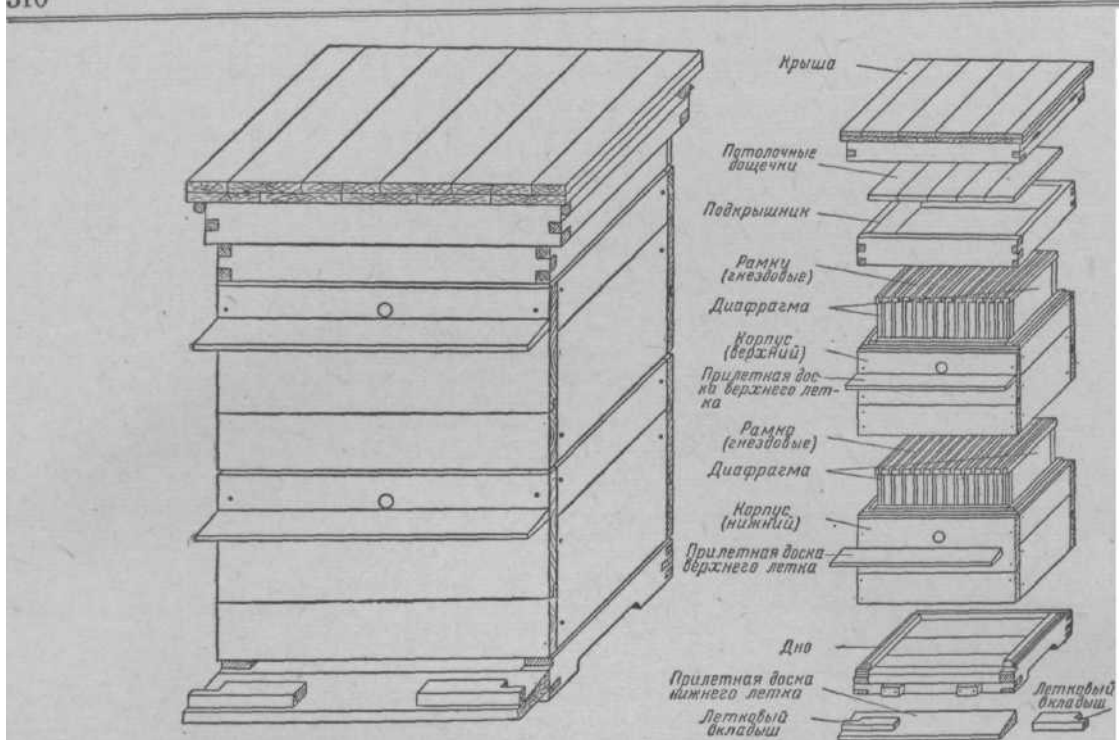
Одностенный двухкорпусный улей (общий вид и детали устройства).
